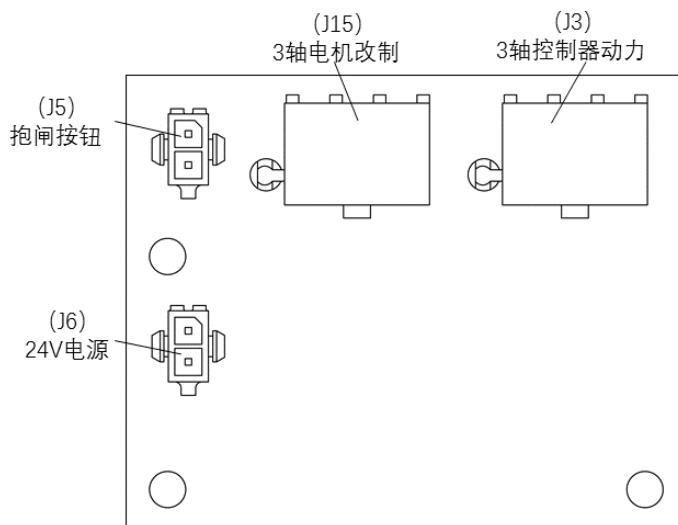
第二机械臂抱闸 PCBA 拆卸示意图
